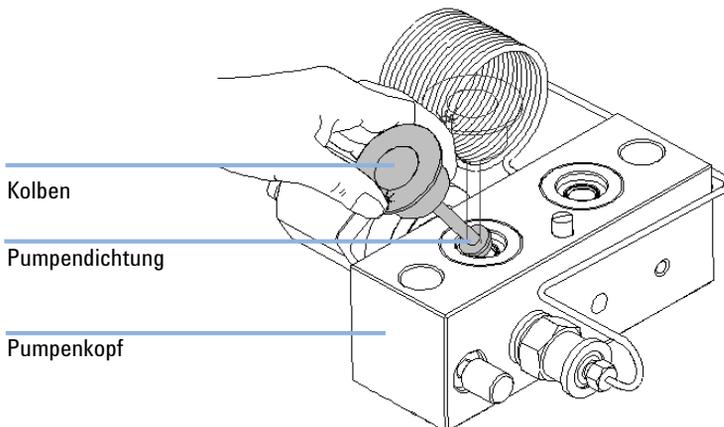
Entfernen der Pumpendichtungen aus dem Pumpenkopf
